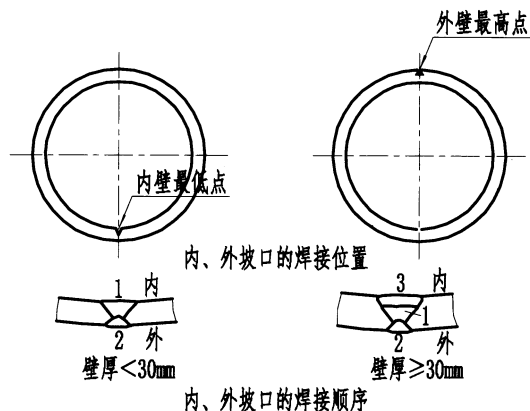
圆管纵缝的焊接位置及焊接顺序示意图
